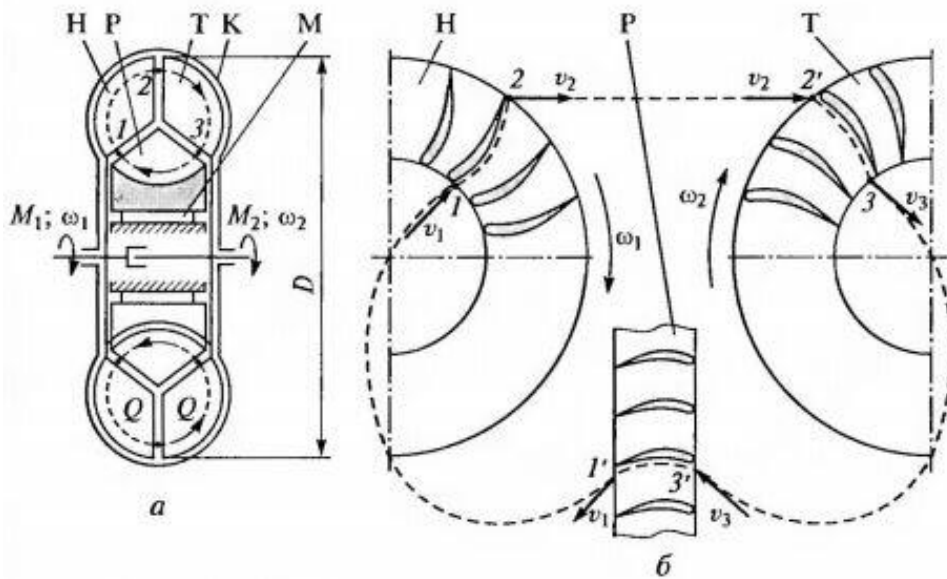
Конструктивная схема гидротрансформатора: а - осевой разрез; б - развертка лопастной системы; Н - насосное колесо; Т - турбинное колесо; Р - реактивное колесо (реактор); К - корпус; М – муфта свободного хода.
